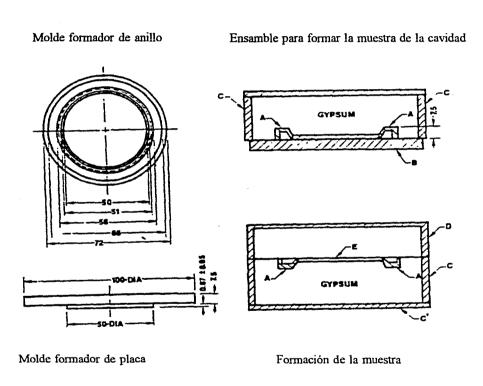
Sistema para formar resinas termocurables. A, molde formador de anillo; B, molde formador de placa; C, frasco superior de dentadura; D, frasco inferior de dentadura, E, muestra, molde formador de anillo y placa de acero inoxidable. Dimensiones en milímetros.
